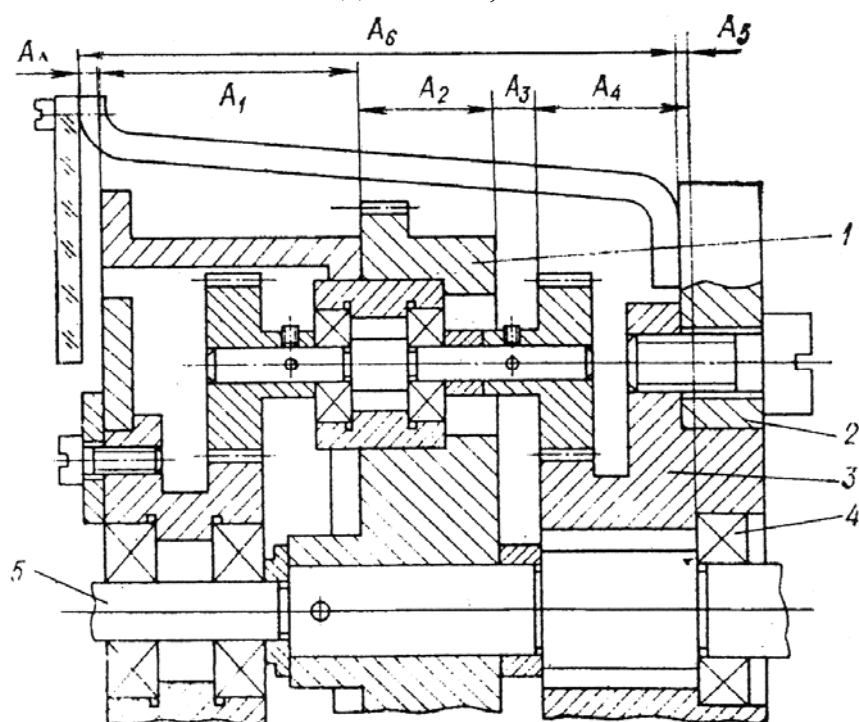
Узел подшипникового соединения: 1 – водило; 2 – плита; 3- колесо;
